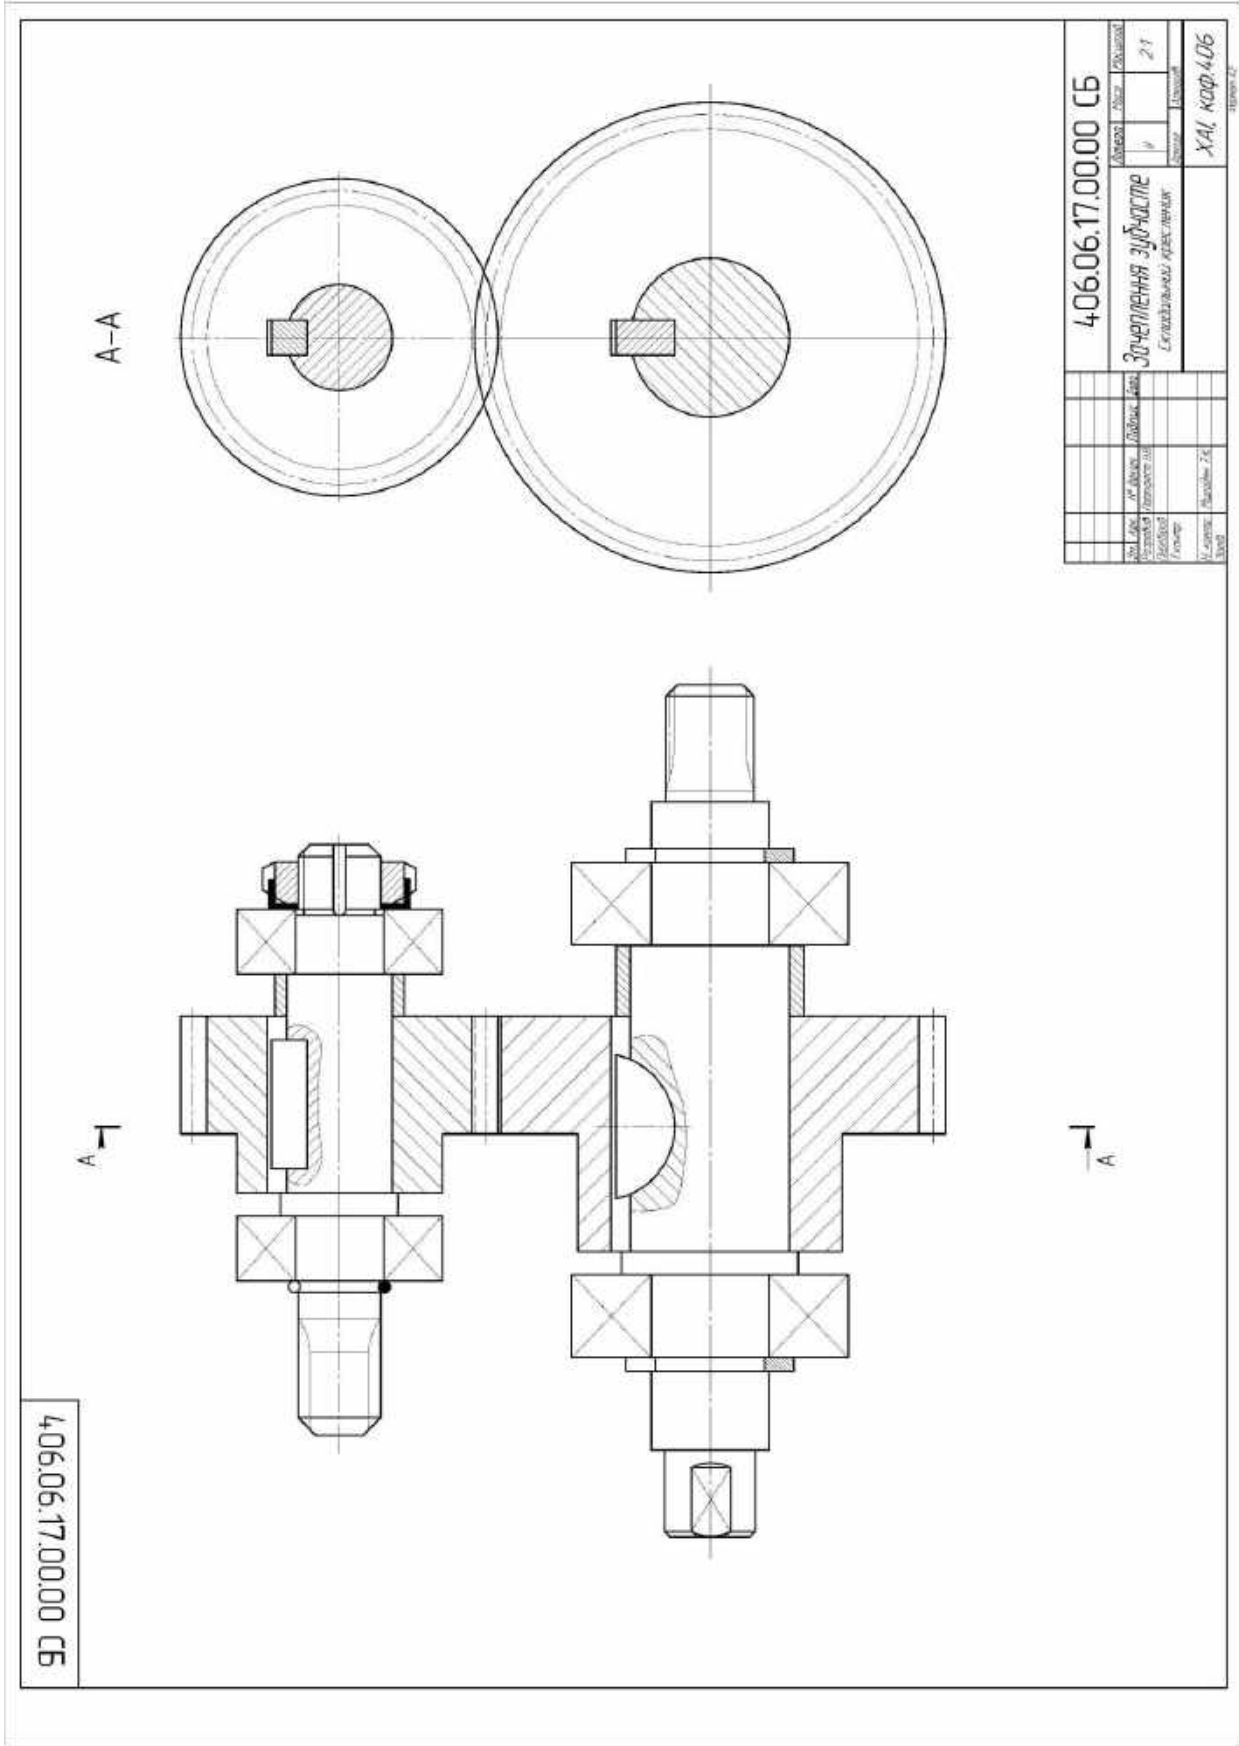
Шостий етап виконання складального креслення зубчастого зачеплення з підшипниками
